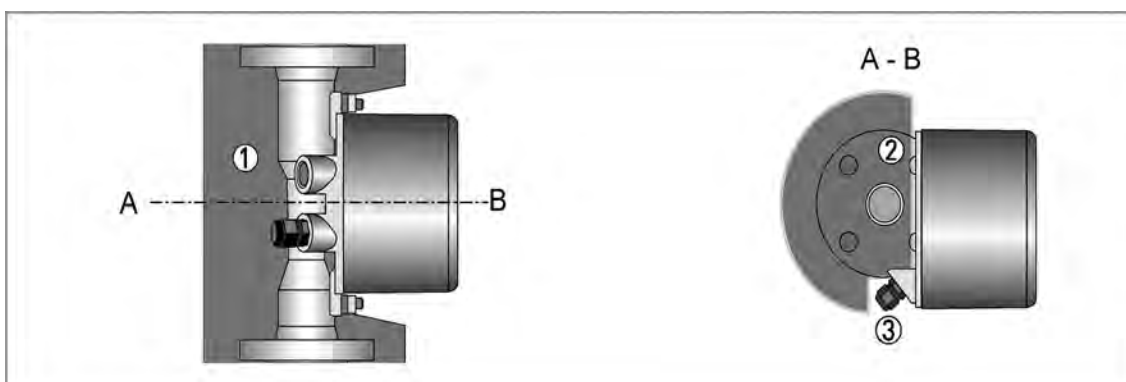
Тепловая изоляция - поперечное сечение
